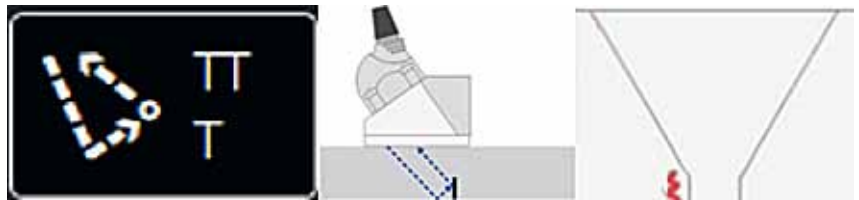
Tipo de onda elegida y fisura por localizar en la zona del talón de la soldadura.
